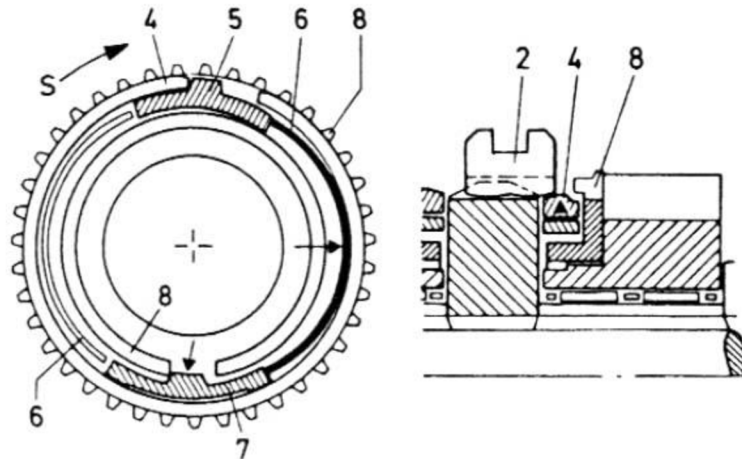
Synchronizace se servoučinkem - řazení za klidu: 1- těleso synchronizace; 2- řadičí objímka; 4- synchronizační kroužek; 8- těleso spojky; 9- ozubené kolo [12]
